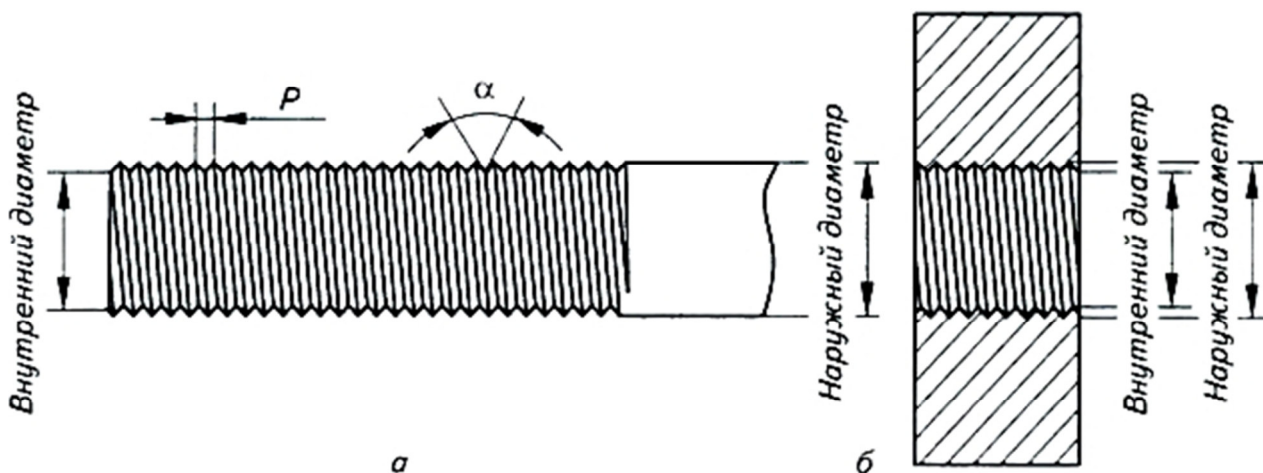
Элементы резьбы: а — наружной; б — внутренней
